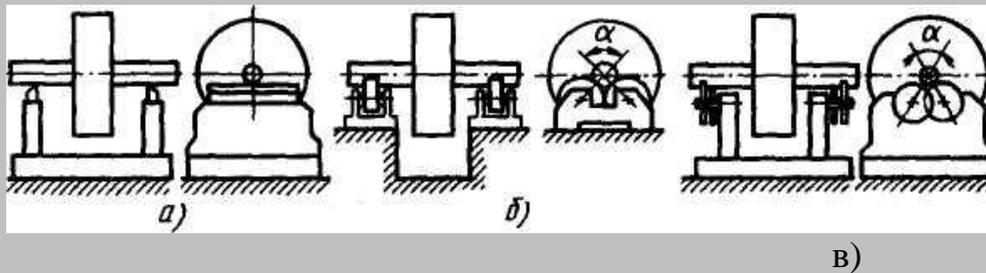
Устройства для статической балансировки шкивов ременной передачи: а — с параллельными призмами, б — роликами, в — дисками
